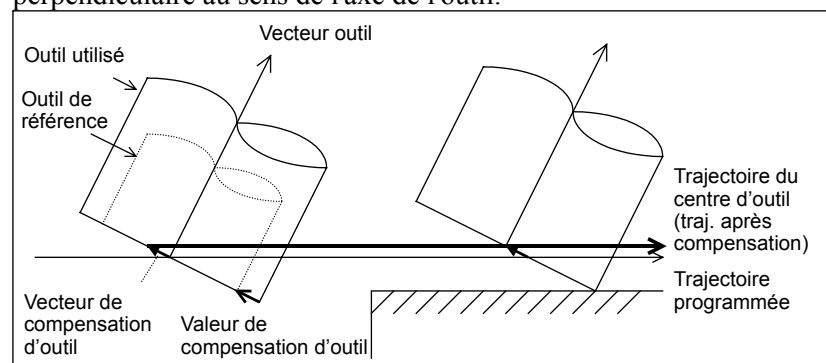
(a) Correction du bord d'attaque
